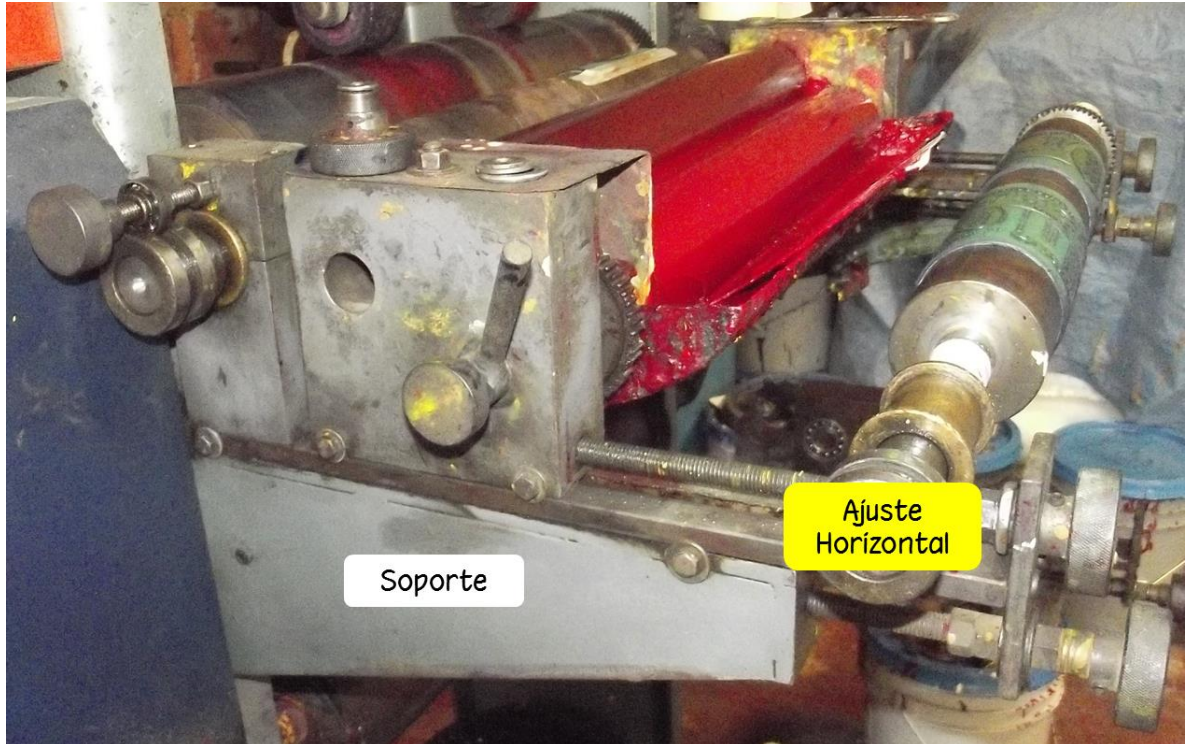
Vista Mecanismo de Ajuste Horizontal y del soporte del sistema de impresión.
